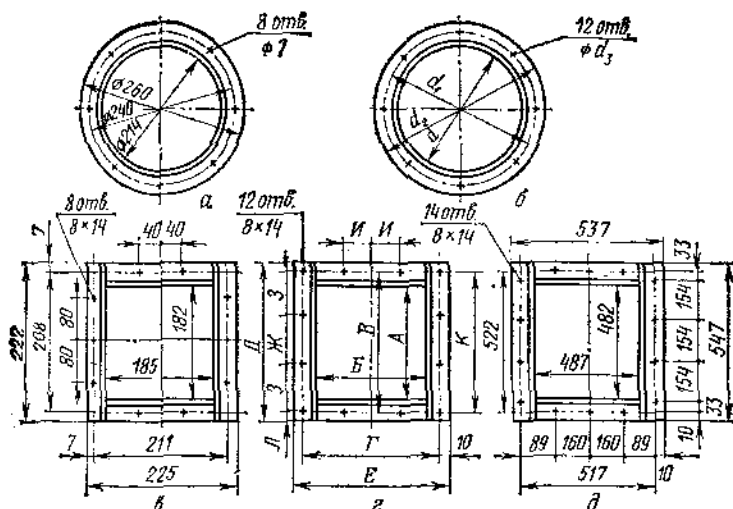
Фланцы к вентилятору типа ВЦП:
